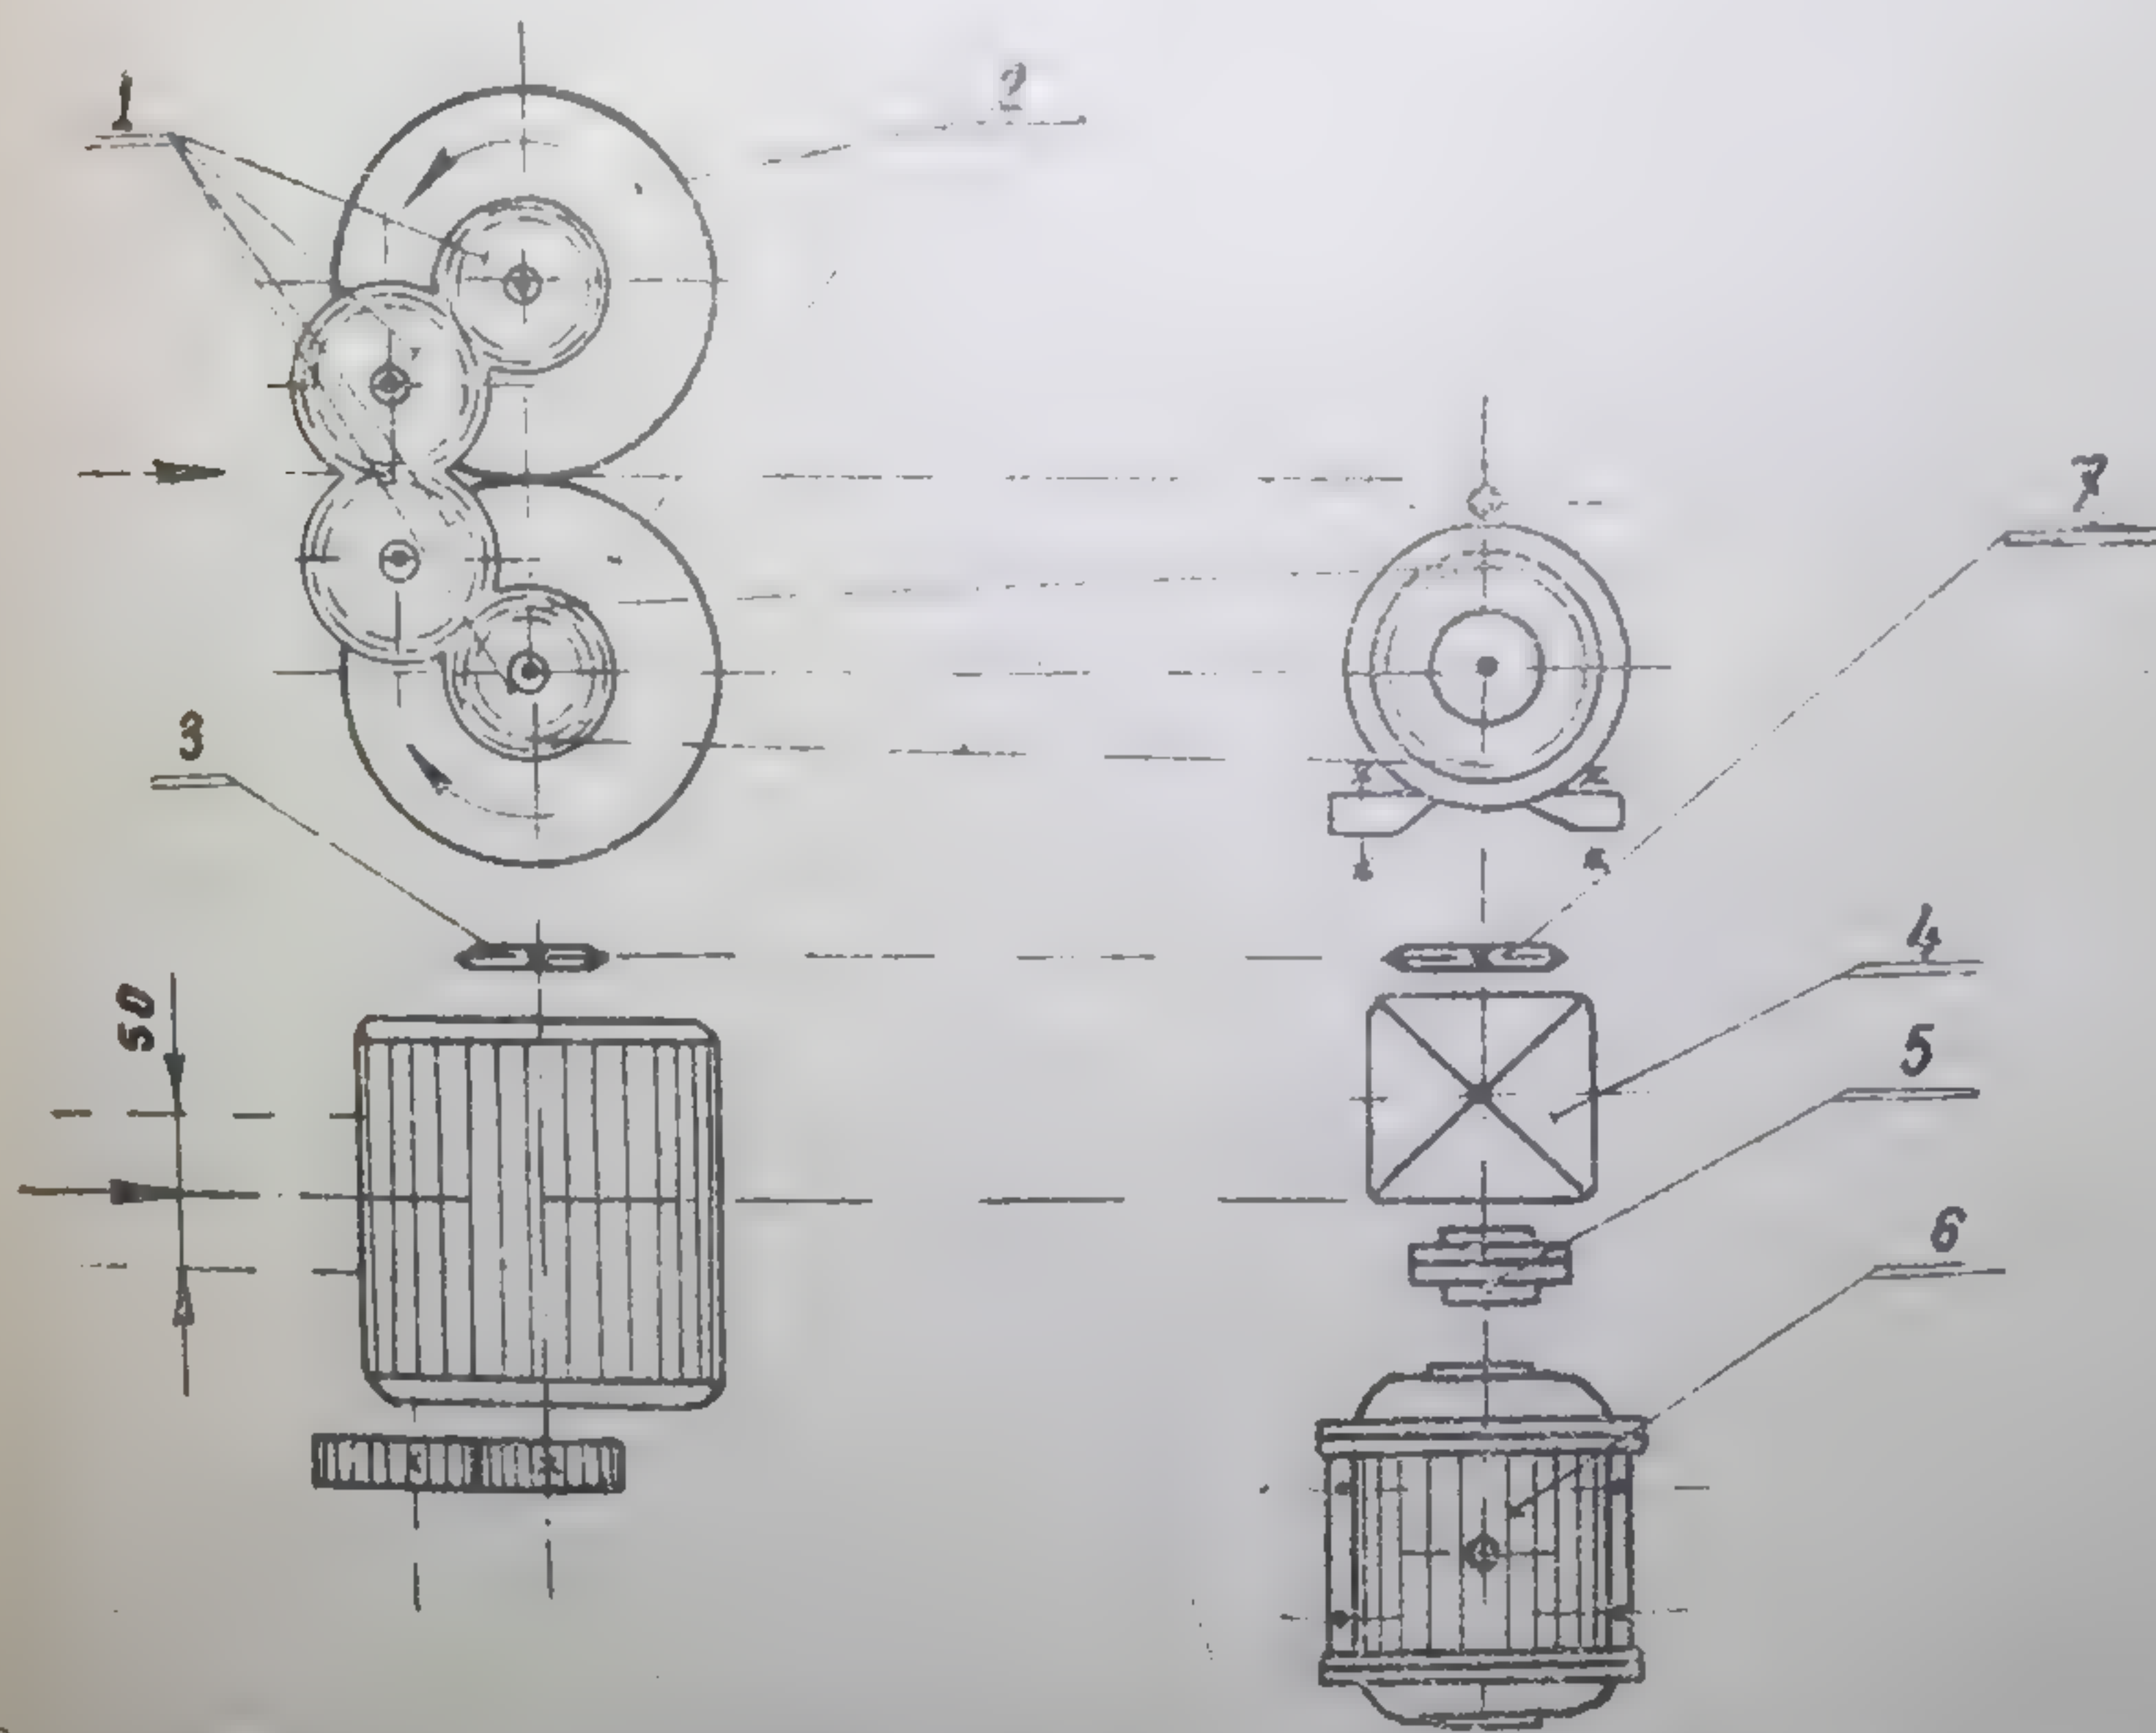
Схема однопарвальной плющильной установки для солом конопли: 1 — шестерни цилиндрические, 2 — гладкие валцы, 3 — звездочка, 4 — редуктор, 5 — полумуфты, 6 — электромотор, 7 — звездочка.
